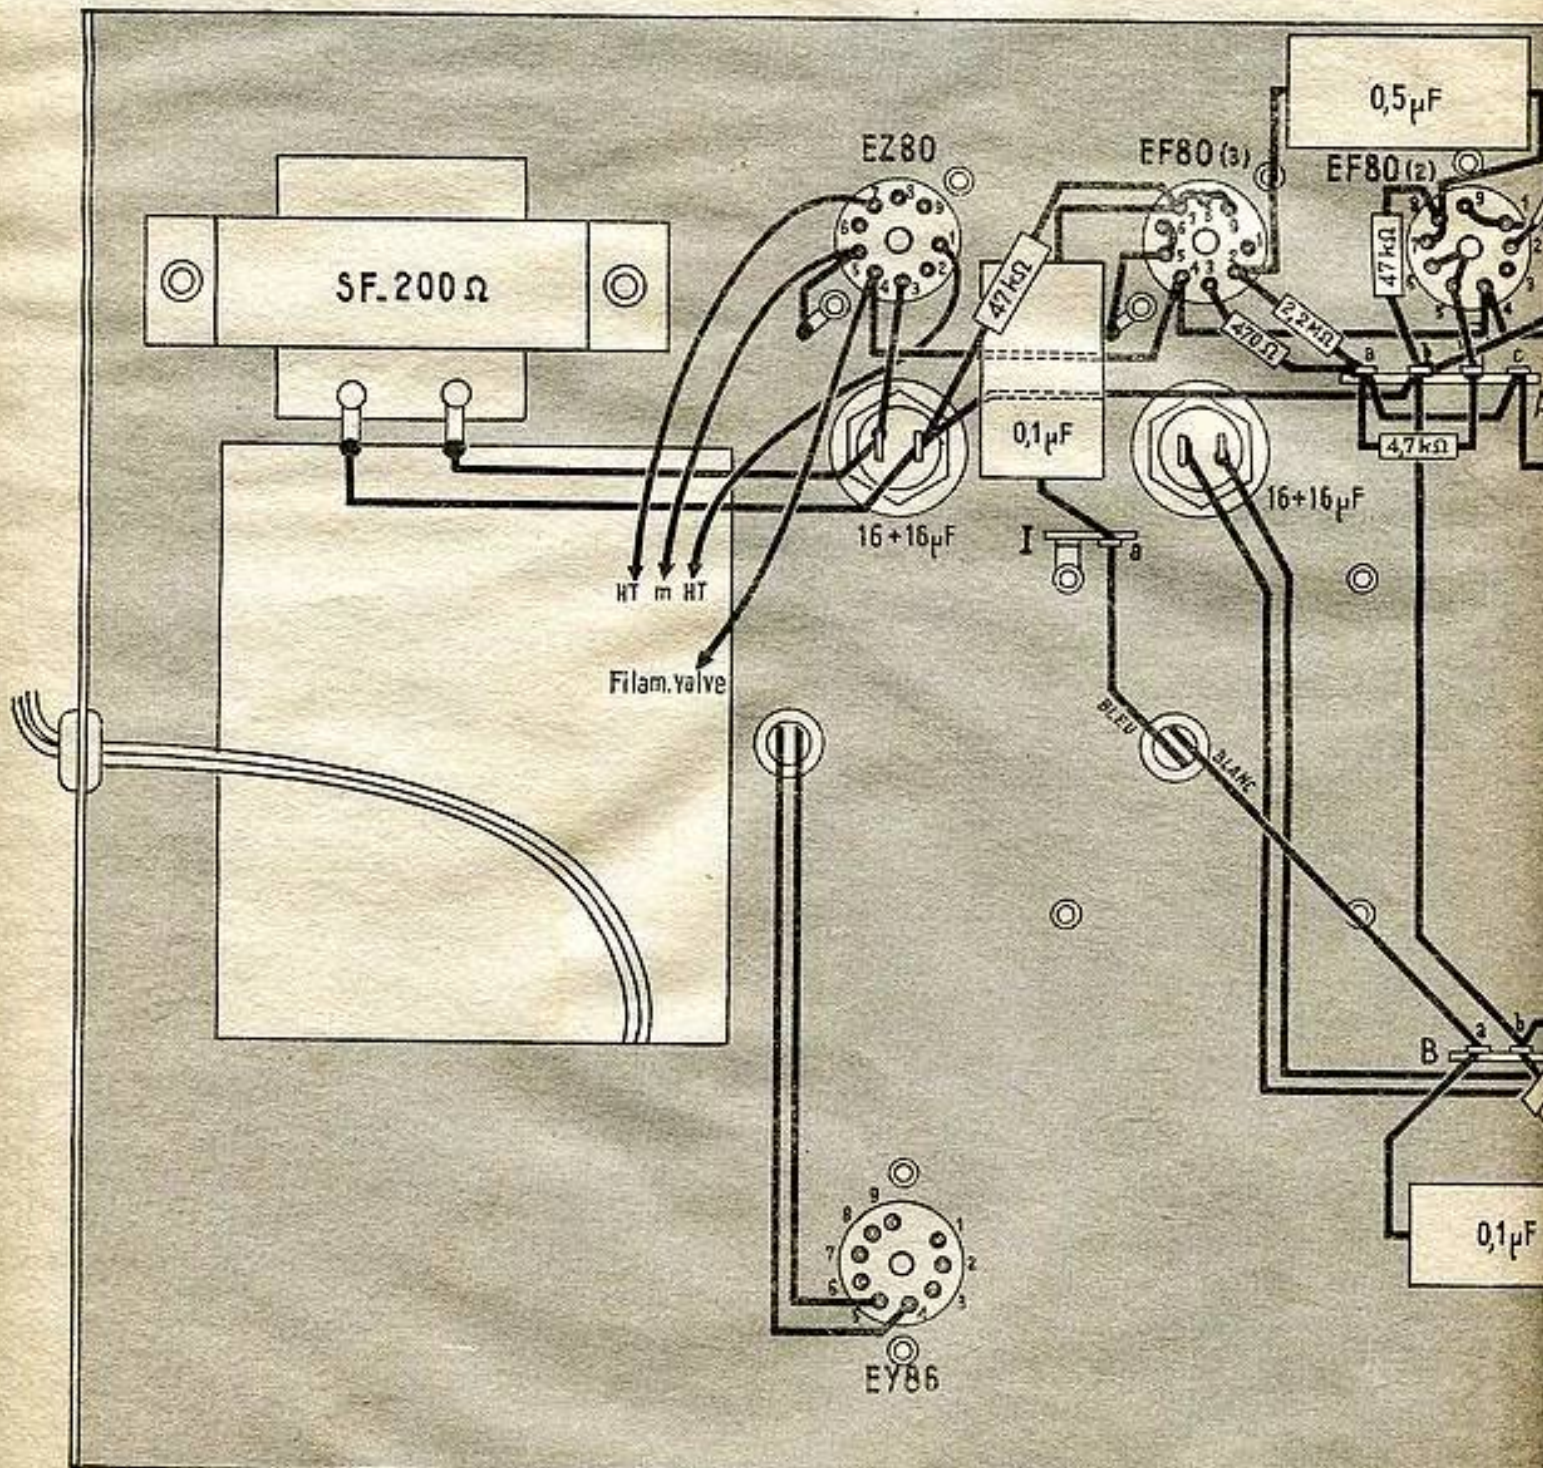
CABLAGE DU CHASSIS HORIZONTAL (DESSOUS)
